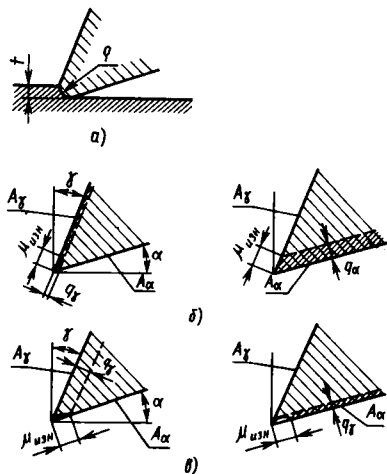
Изнашивание инструмента и поверхности его заточки
